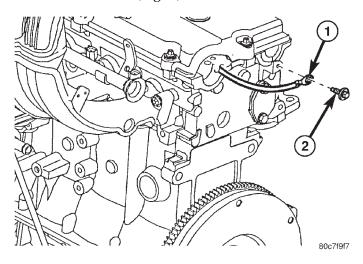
TIRA DE MASA A MOTOR - 2.4L
